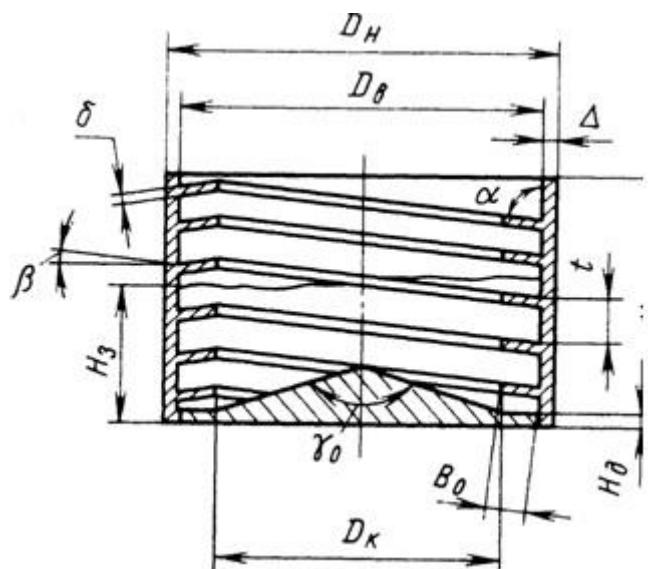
Конструкция цилиндрической чаши ВБЗУ
